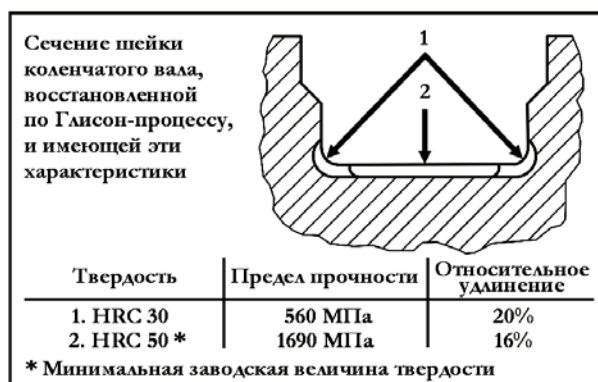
Физико-механические свойства металла восстановленного коленчатого вала после наплавки двумя проволоками (компания «Gleason Engineering Industries, Inc.»): 1 – зоны галтелей; 2 – зона рабочей поверхности шейки [12]
